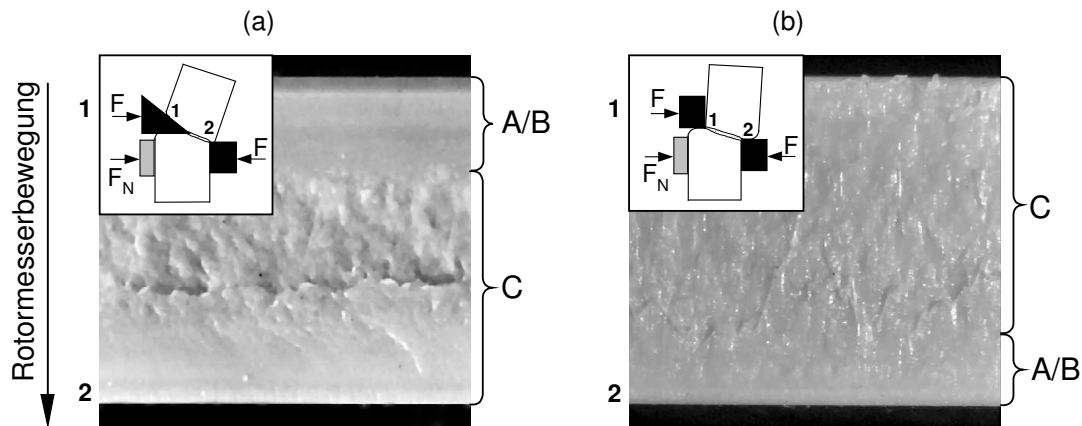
Bruchflächen zerkleinerter Probekörper aus Polypropylen (Wanddicke 5 mm) durch Schneid- (a) und Scherbeanspruchung (b)
